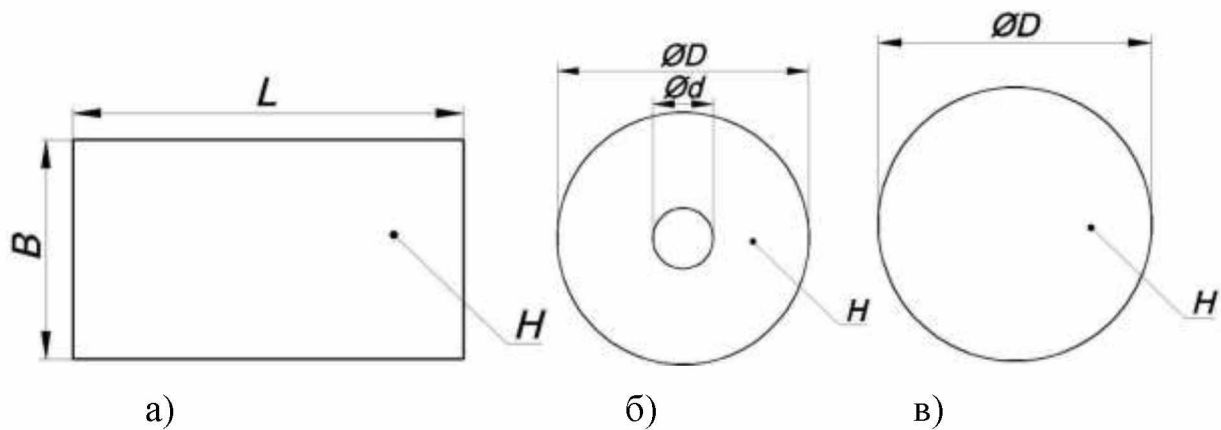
Ескізи типових заготовок: а) «Плита»; б) «Фланець»; в) «Вал»
